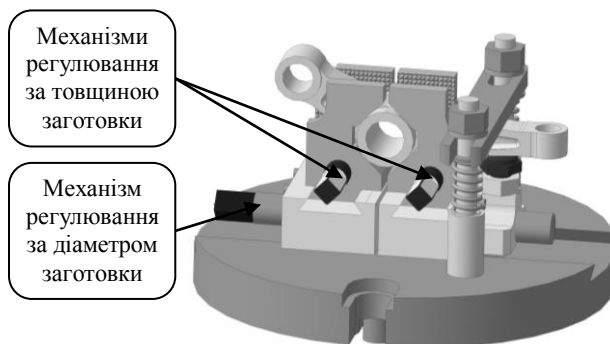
Переналаджуваний установлювально-затискний модуль для обробки деталей типу важелів
